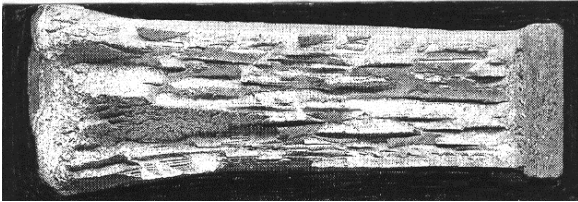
Расщепления в изломе образца ИППГ стали X70 / Fig. 1. DWTT specimen fracture of steel X70 with laminations [10]
